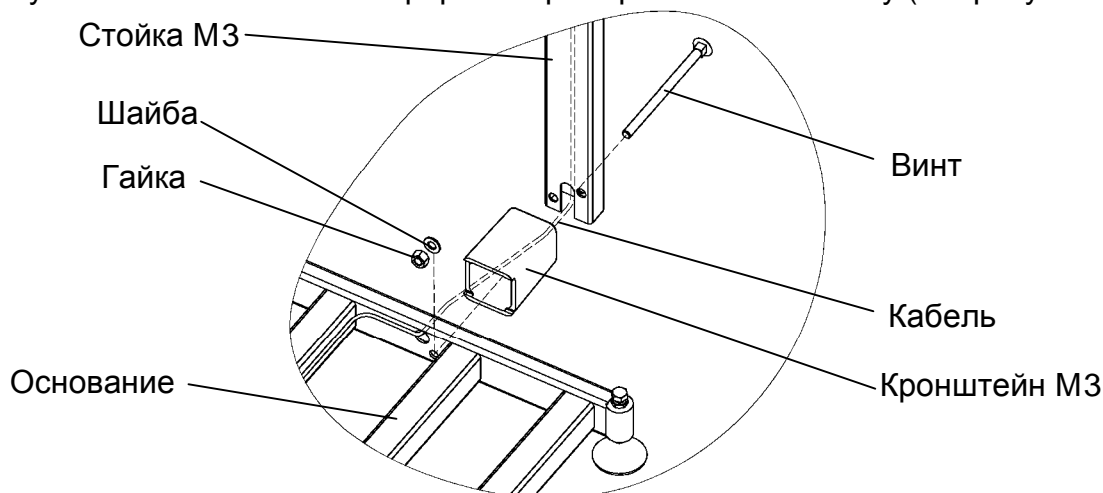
Крепление прямоугольной стойки к основанию весовой платформы ТВ-М_А
